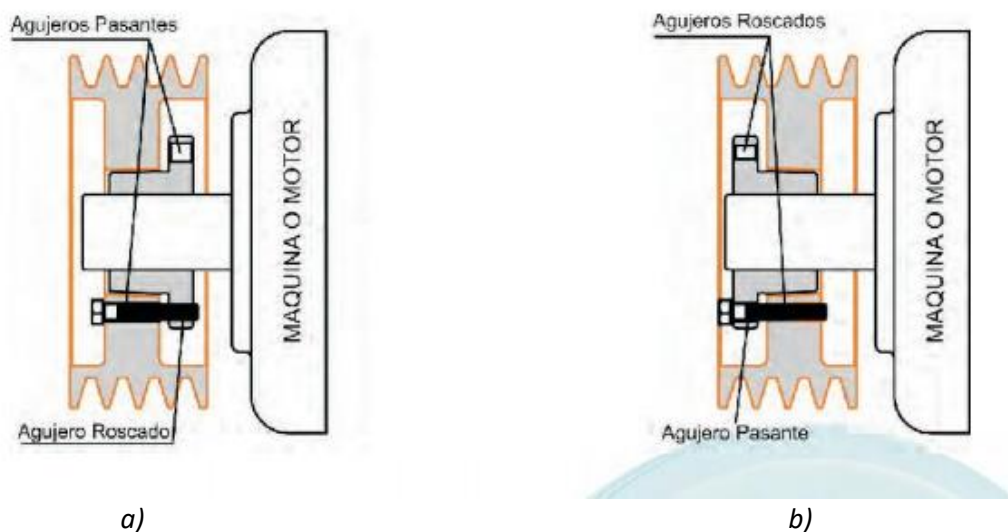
Vista de sección y maneras de montar el sistema. a) Montaje estándar. b) Montaje reverso
